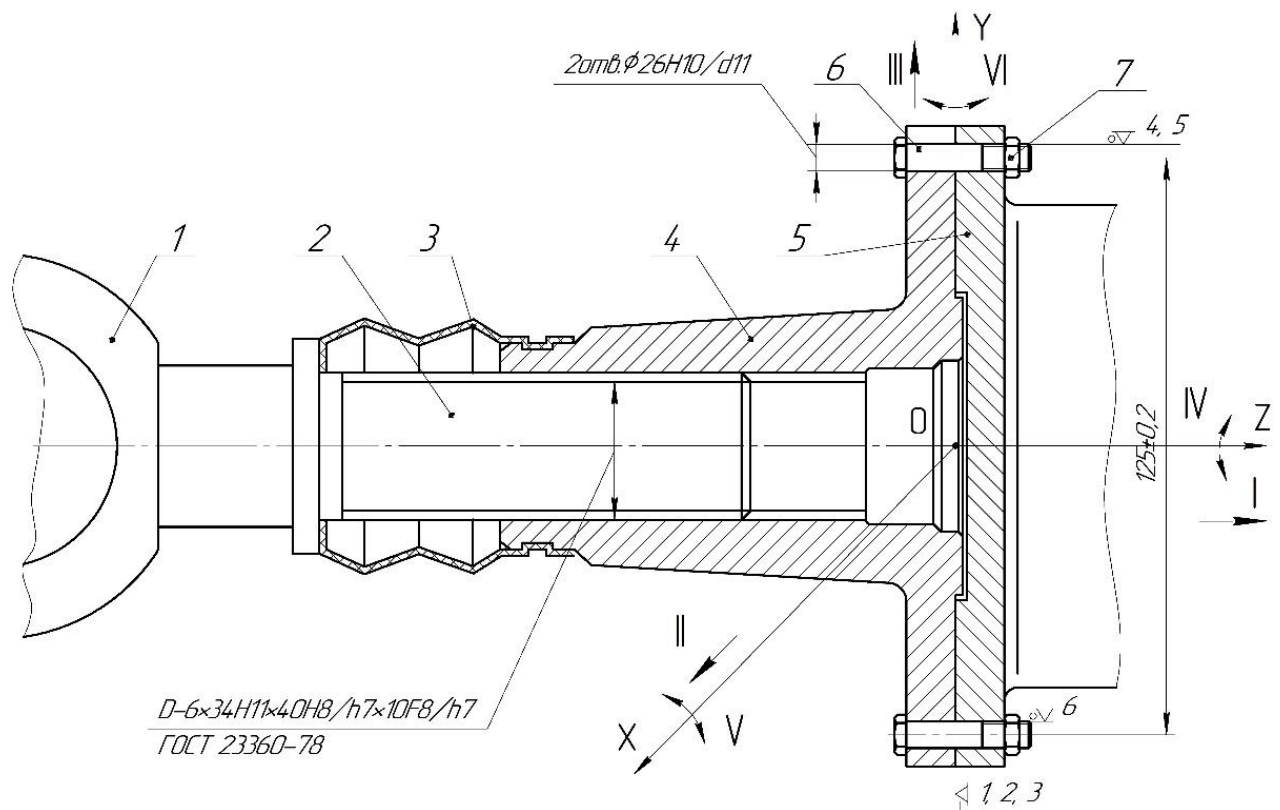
Карданний вал трактора: 1 – вилка переднього шарніру;
